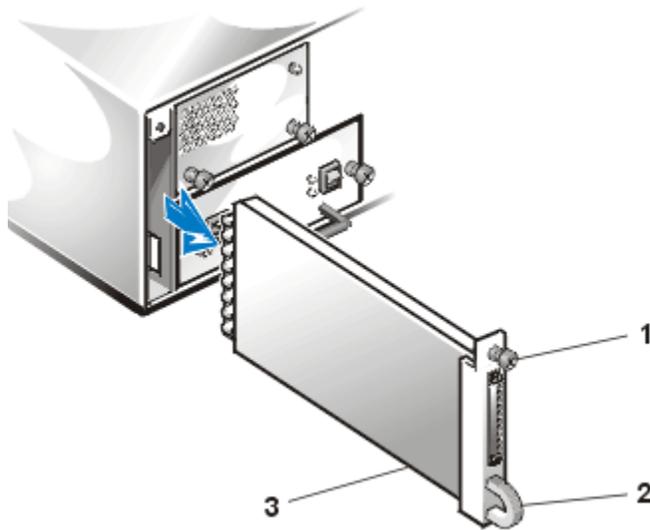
Desmontaje del módulo existente (lado izquierdo)
